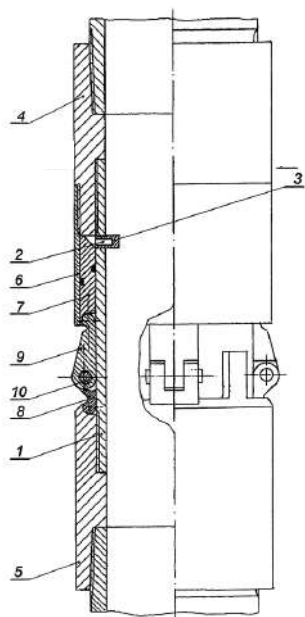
Центратор гидравлический [1]: 1 – корпус; 2 – сквозные радиальные каналы; 3 – разрушаемые пробки; 4, 5 – муфты; 6 – рабочий цилиндр; 7 – поршень; 8, 9 – основные и дополнительные центрирующие элементы; 10 – шарнирные соединения
